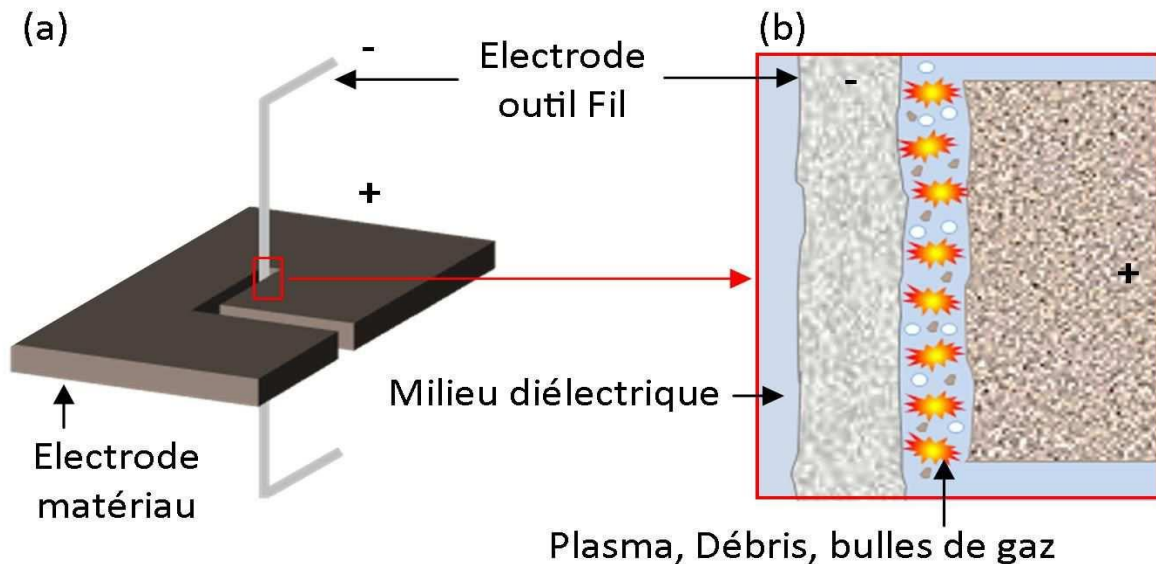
Principe d'usinage par Electroérosion à fil (WEDM). (a) Vue d'ensemble ; (b) Zoom sur la zone d'interaction avec ablation par décharges électriques. [6]
